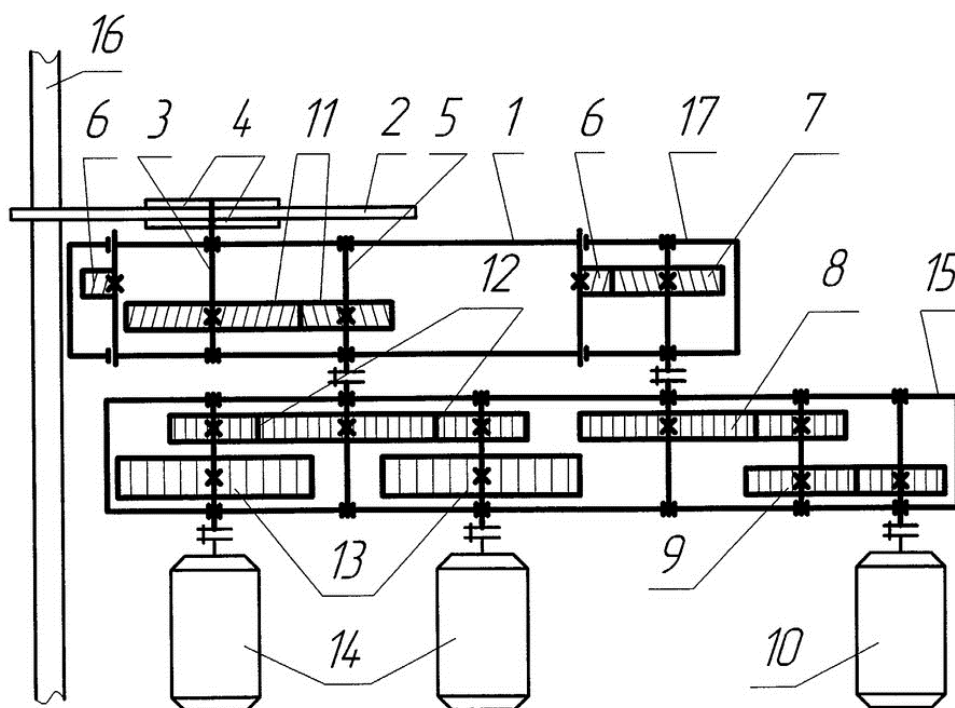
Кінематична схема механізму пили для різання прокату [3]
